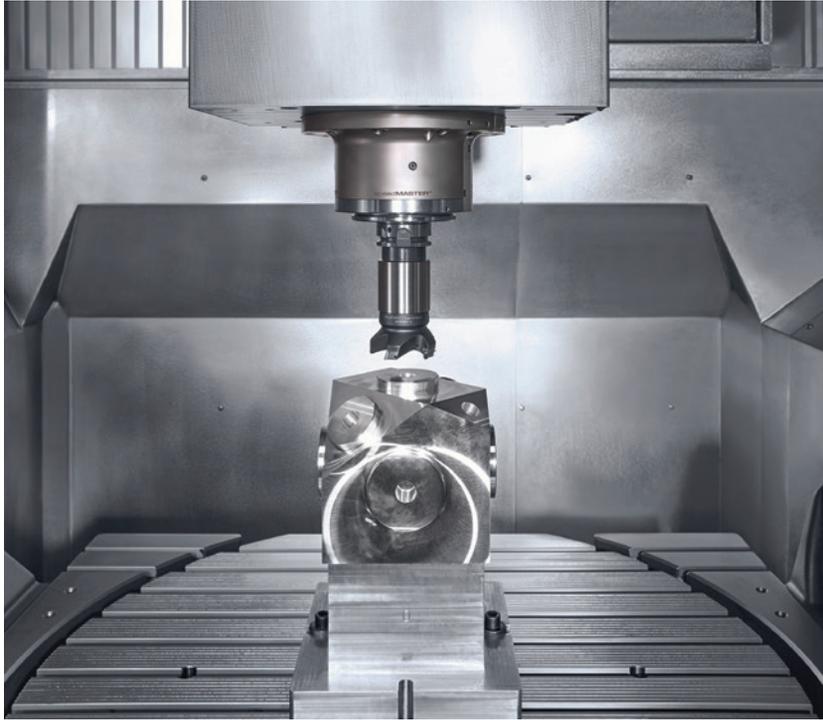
Für die Bearbeitung von Metall werden eine sehr steife Maschine und starke Motoren benötigt. Die Abbildung zeigt die Innenansicht einer DMU 95 monoblock von DMG Mori (© DMG Mori).
